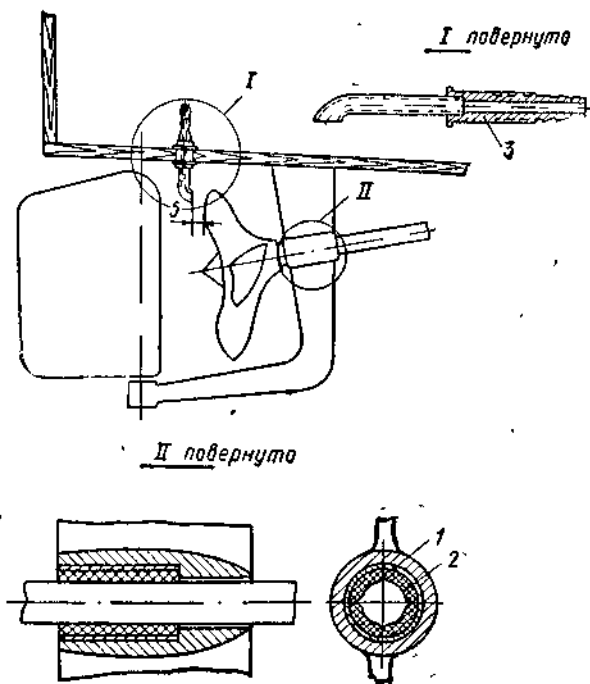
Водозаборник и установка резинометаллического подшипника в кронштейне.
